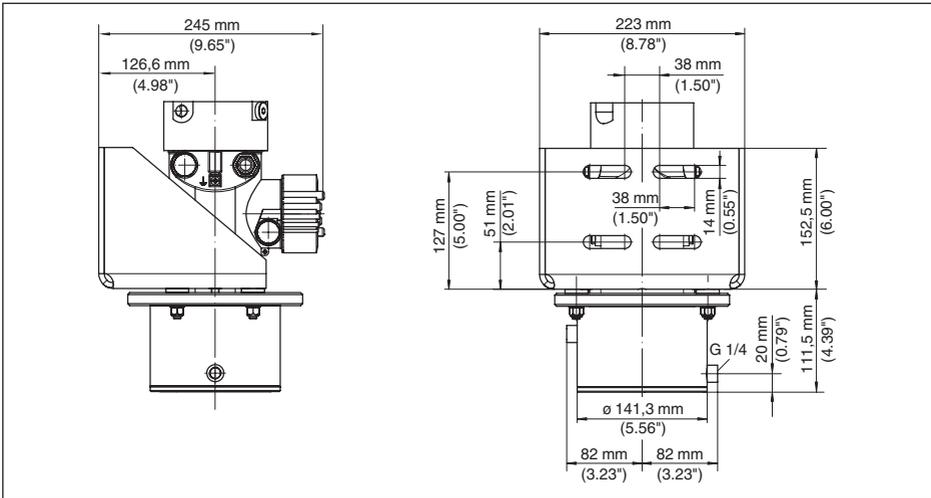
Aktives Wasser-Kühlsystem mit Gehäusekühlung und Gehäuse-Kühldeckel
